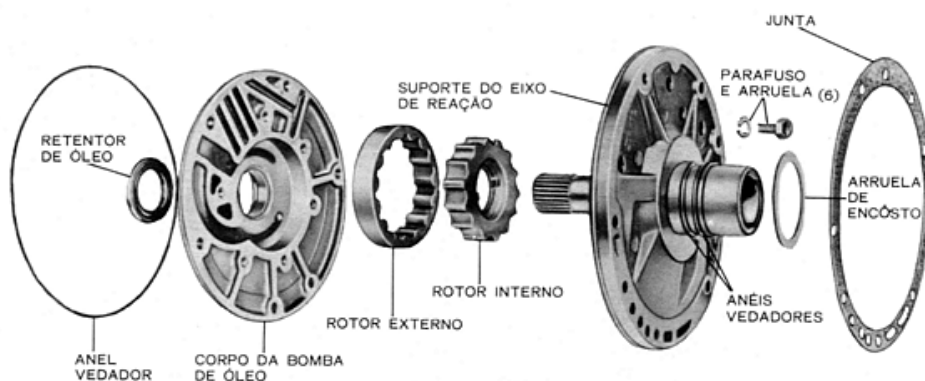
Bomba de óleo e suporte do eixo de reação desmontados
